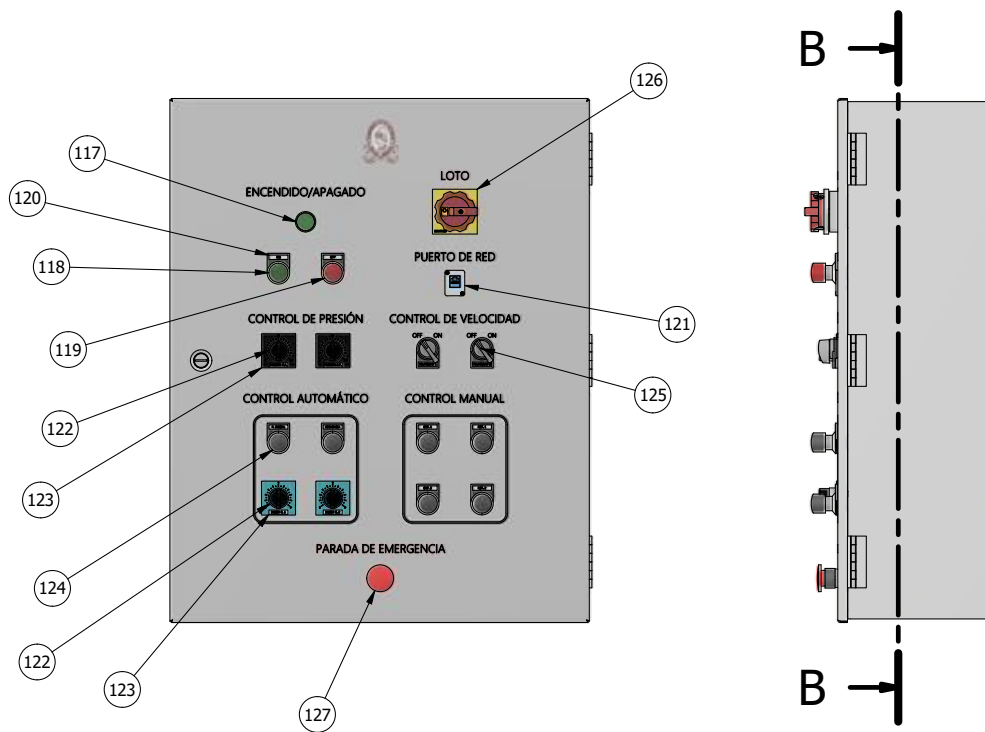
Dibujo explosionado de componentes externos de la prensa.
